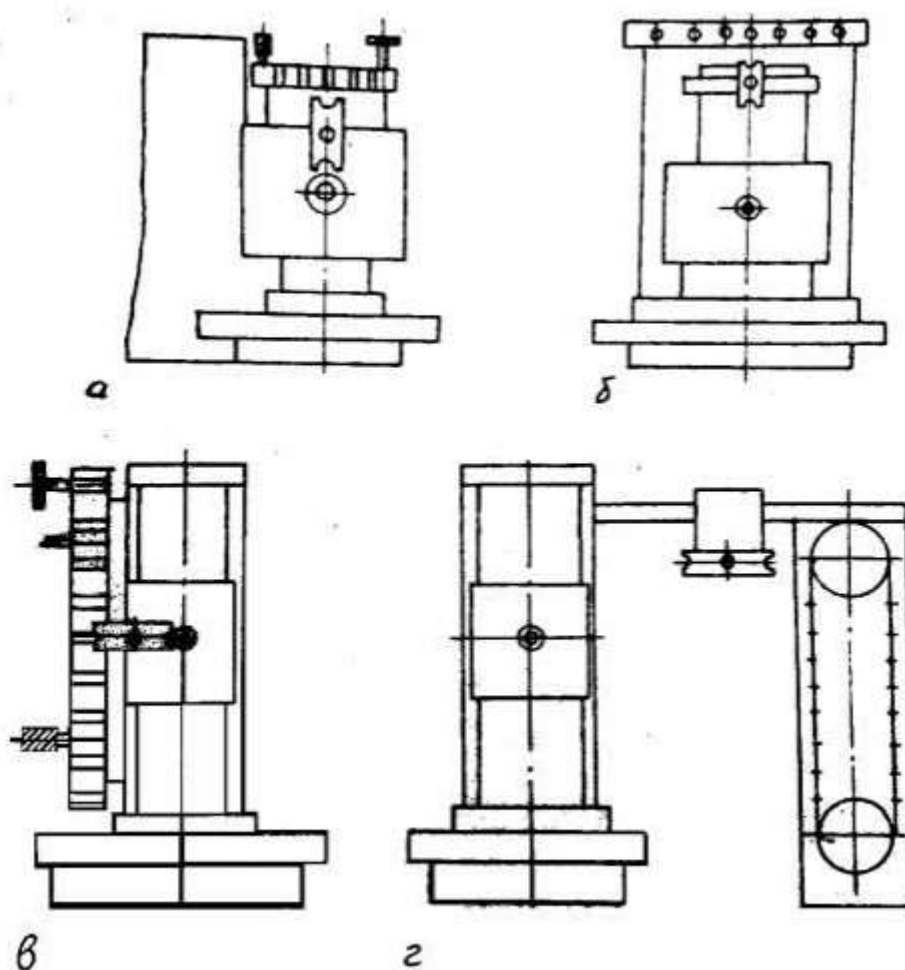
Схеми розташування інструментальних магазинів верстатів з ЧПК на шпиндельній бабці
